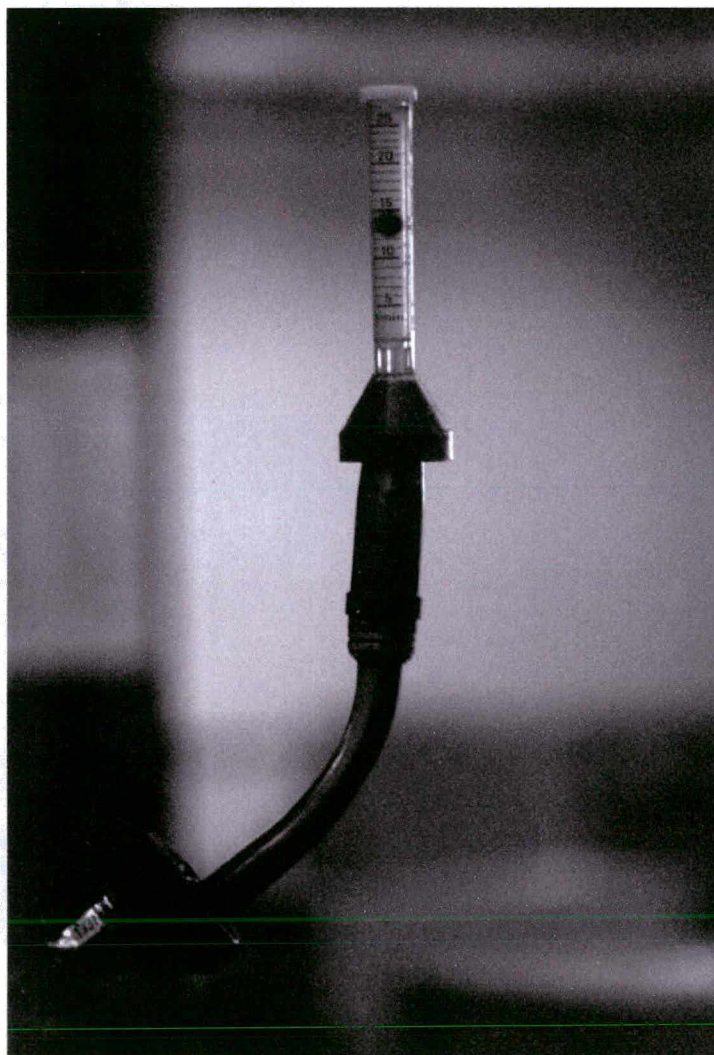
Rotâmetro utilizado no bocal da tocha de soldagem
